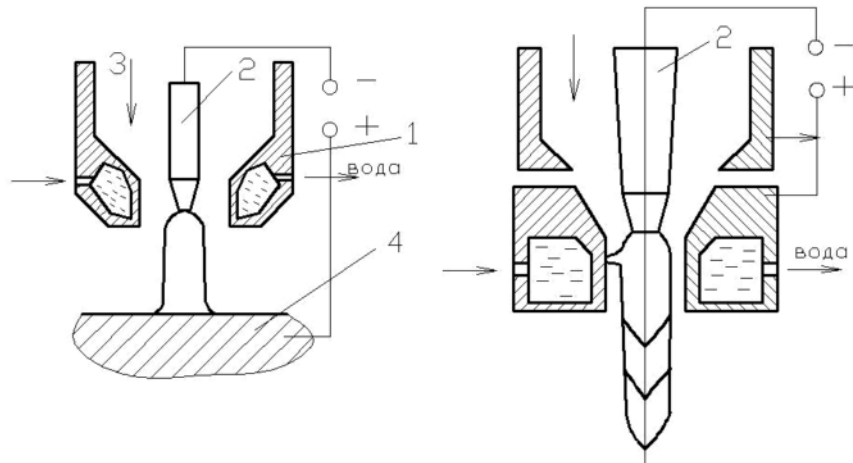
Устройство плазматрона: 1 – сопло; 2 – вольфрамовый электрод; 3 – ввод плазменного газа; 4 – изделие; 5 – канал для подачи присадочного порошка
